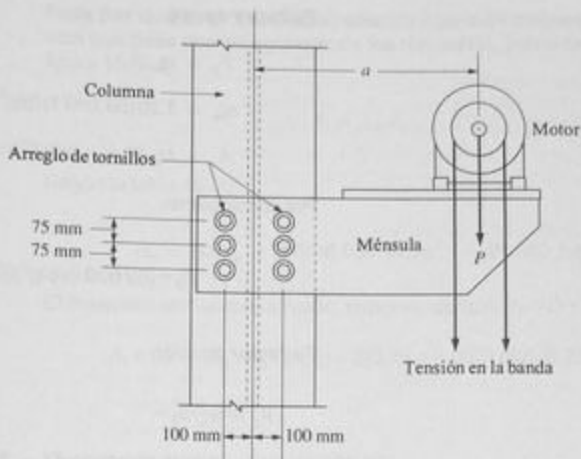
Carga excéntrica en una junta atornillada.
